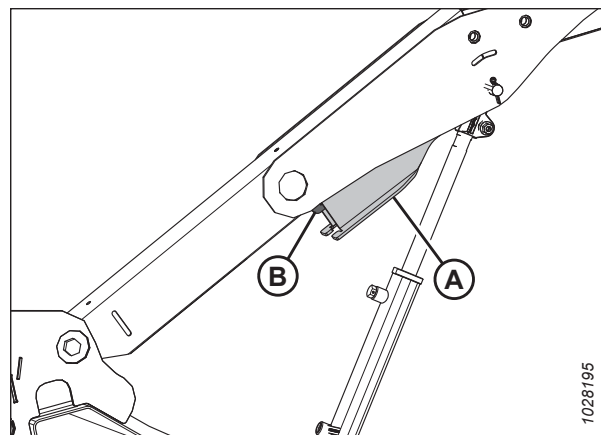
Предохранительный упор мотовила — правый внешний рычаг
